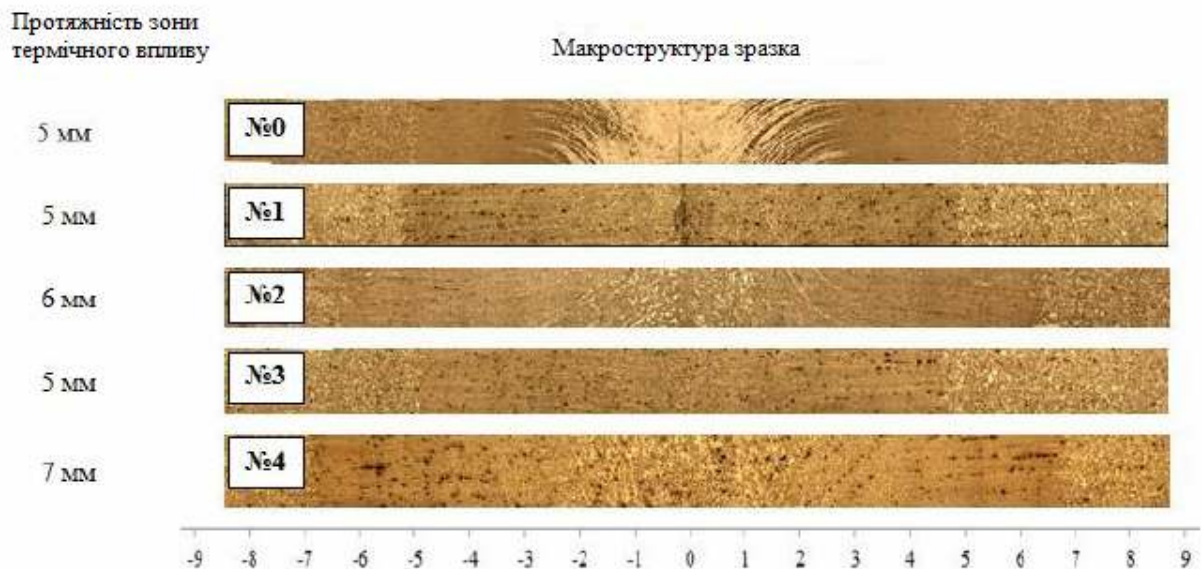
Макроструктура зварного шва зразка сталі E76ХФ
